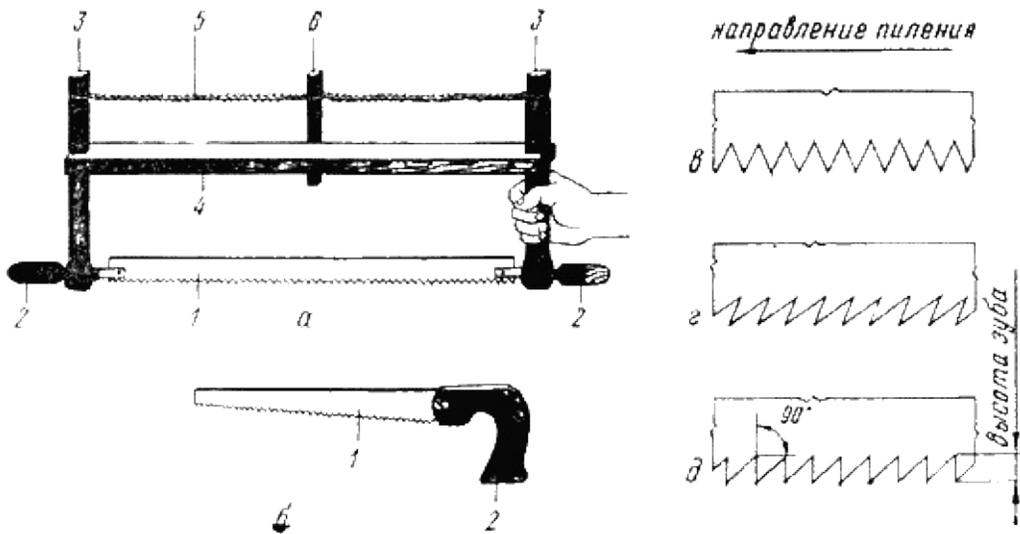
Инструменты для пиления: а — лучковая пила; б — ножовка; в, г, д — зубья пилы; 1 — пильное полотно; 2 — ручка; 3 — стойка; 4 —
